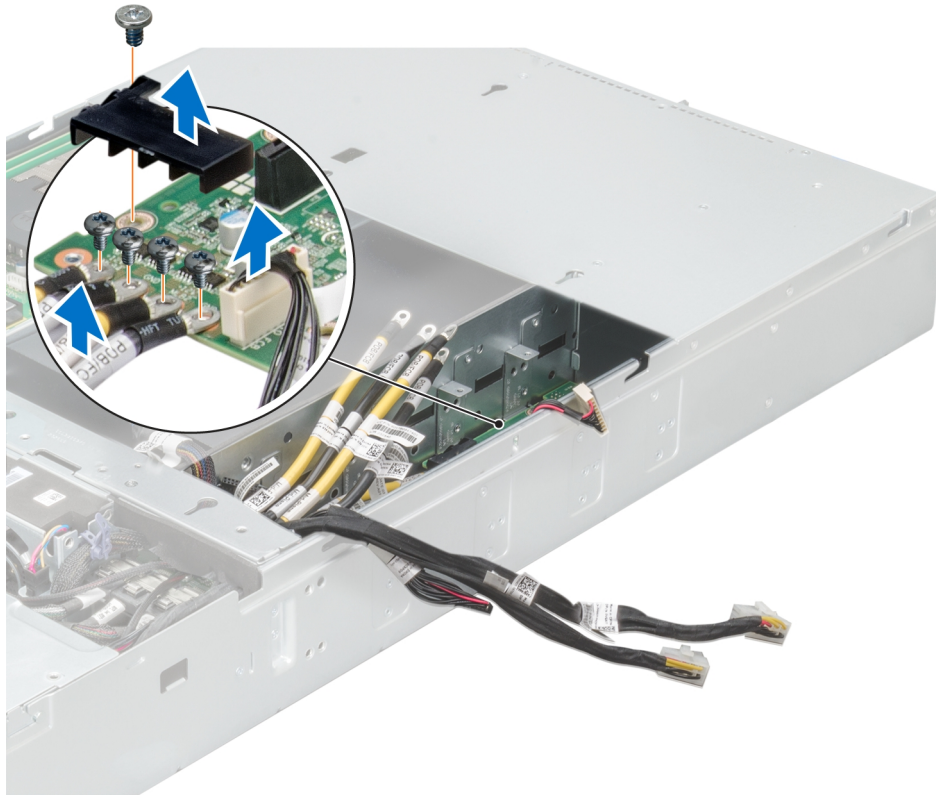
Extracción de la cubierta de cables de alimentación y los cables de alimentación de la PDB 2
